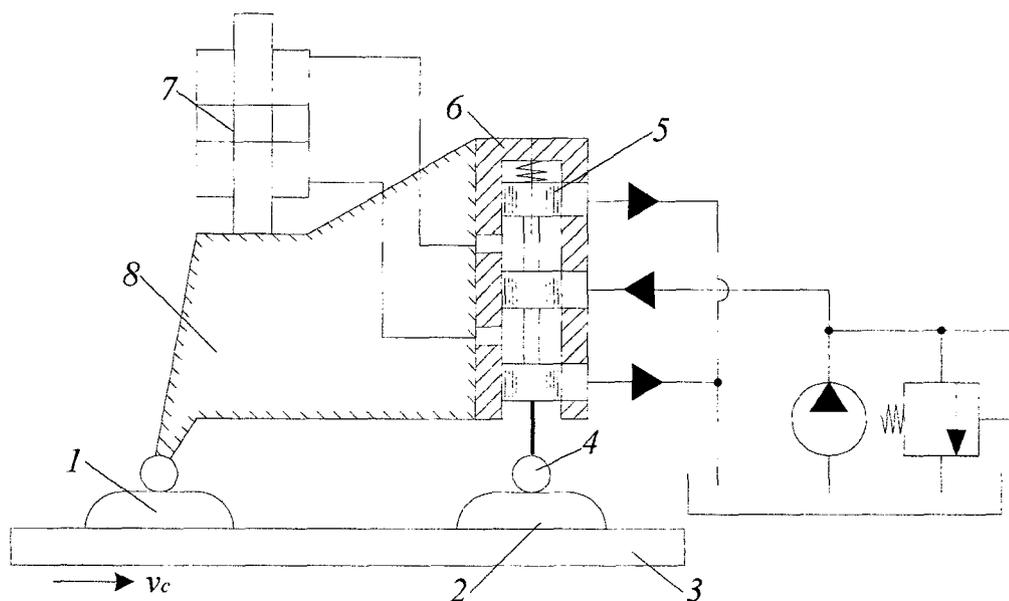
Следящий гидропривод копировального фрезерного станка
